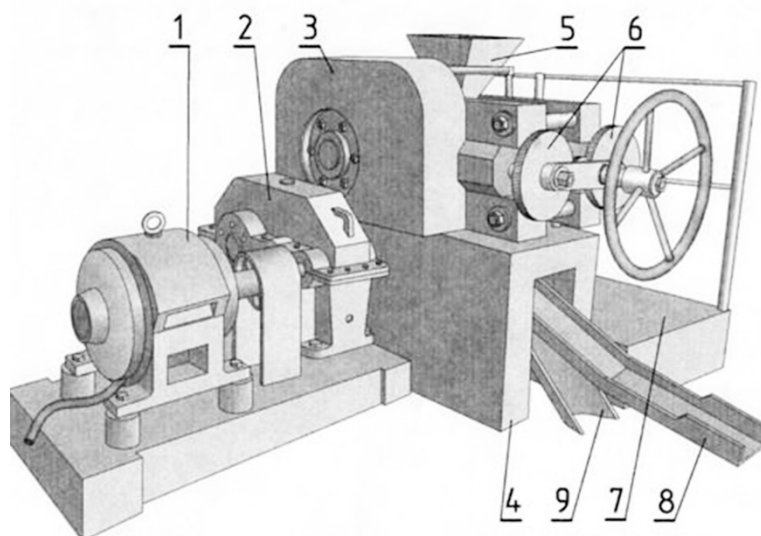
Схема двохвалкового стану для переробки металевої стружки:
